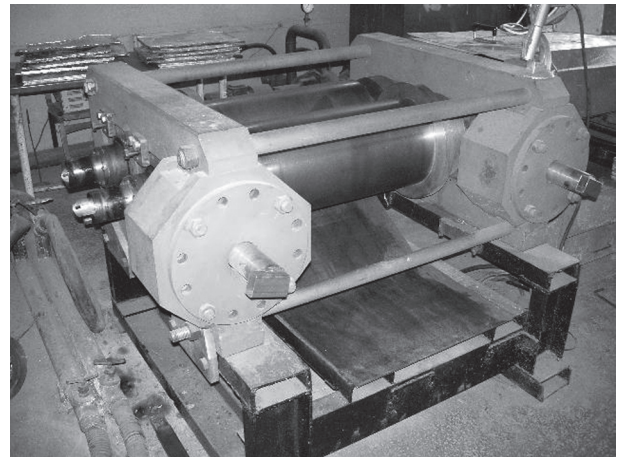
Лабораторная установка беслитковой прокатки свинцовой ленты
